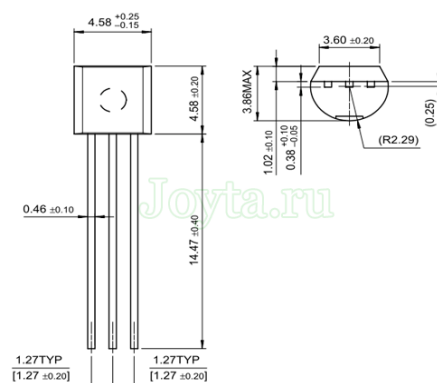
Габаритні розміри стабілізатора 78L05
